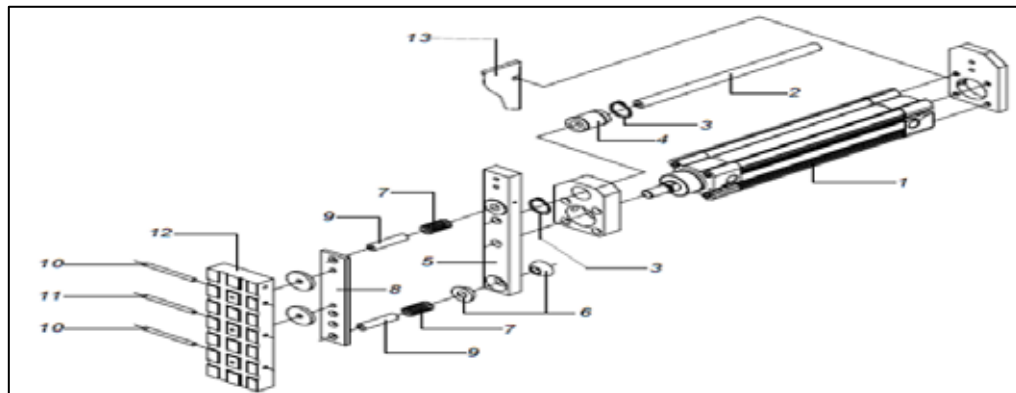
Imagen de Despiece de Equipo: Soldador MOD .431.
